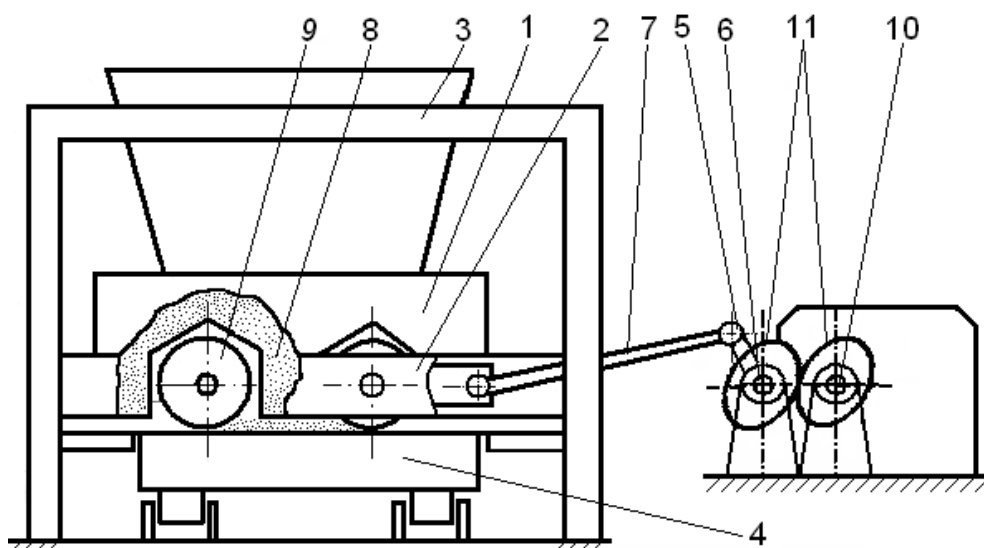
Роликова формувальна установка з кривошипно-повзунним приводом з використанням еліптичної зубчастої передачі
